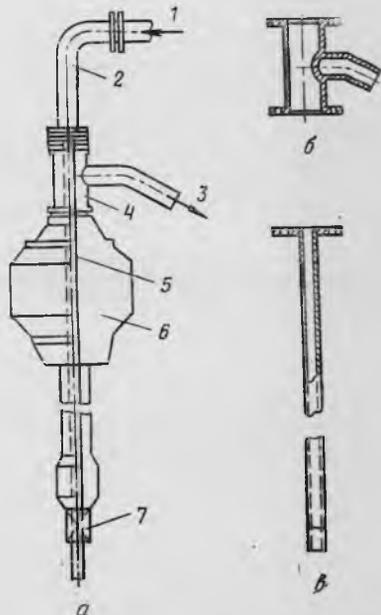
Схема монтажа вертлюжной приставки для станков УВВ-600:
